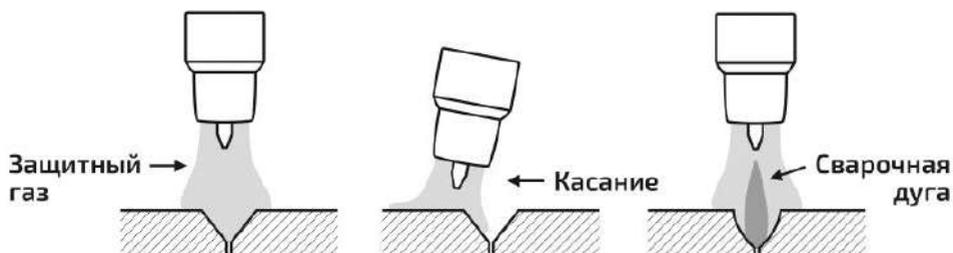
Процесс образования сварочной дуги.
